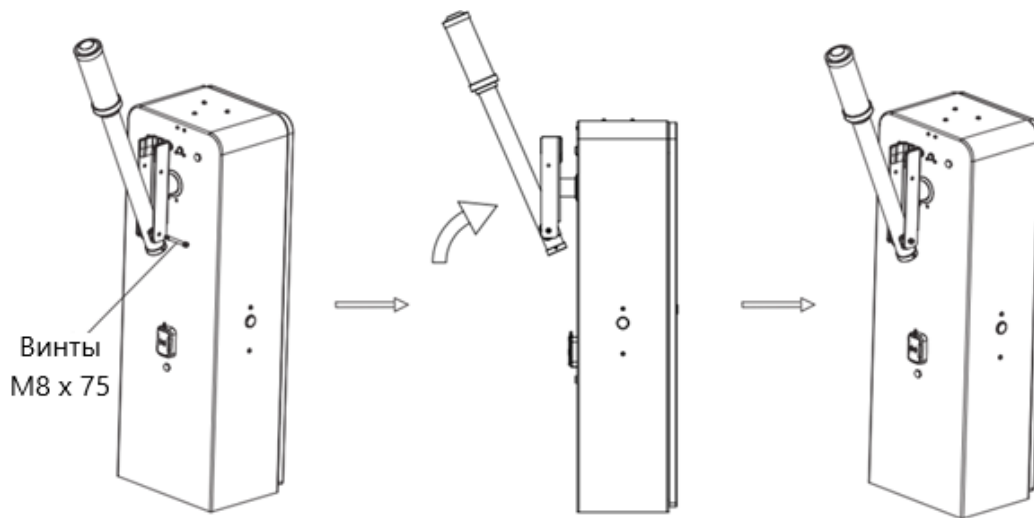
Установка цилиндрической стрелы с защитой от столкновений
